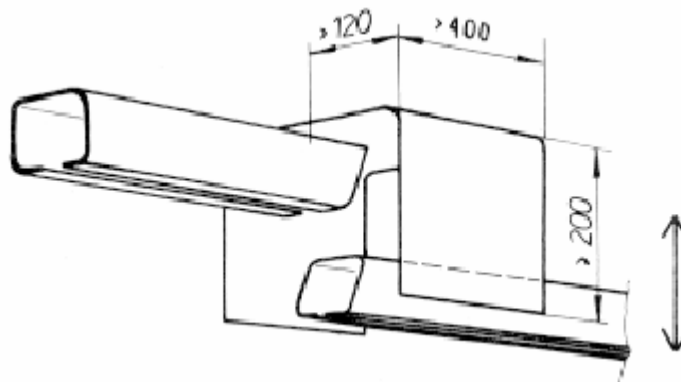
Schutzabdeckung vor der Übergangsstelle eines ausfahrbaren Schienenstückes.
